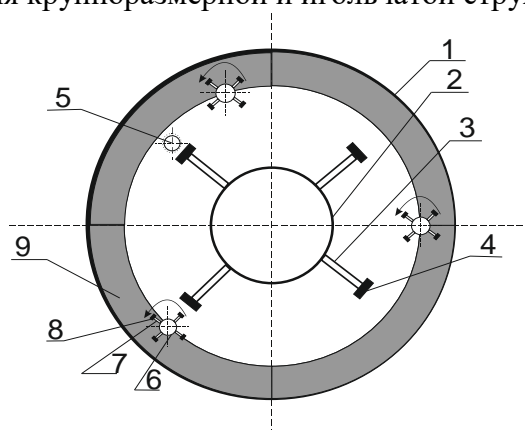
Поперечный разрез быстроходного смесителя для смешивания стружки со связующим
